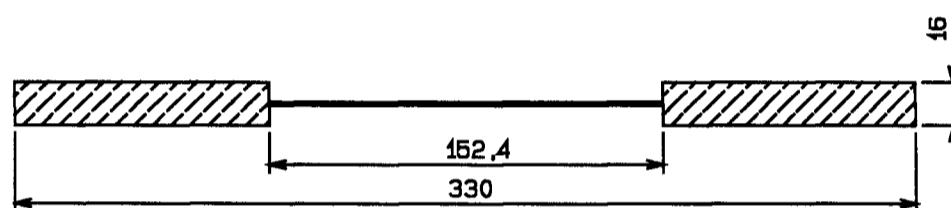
Corpo-de prova do fio para ensaio de tração.
